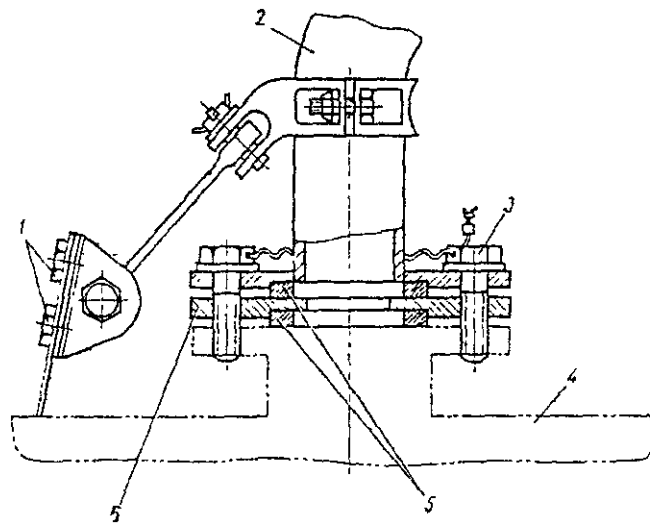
Установка патрубка отбора воздуха на ПОС:
